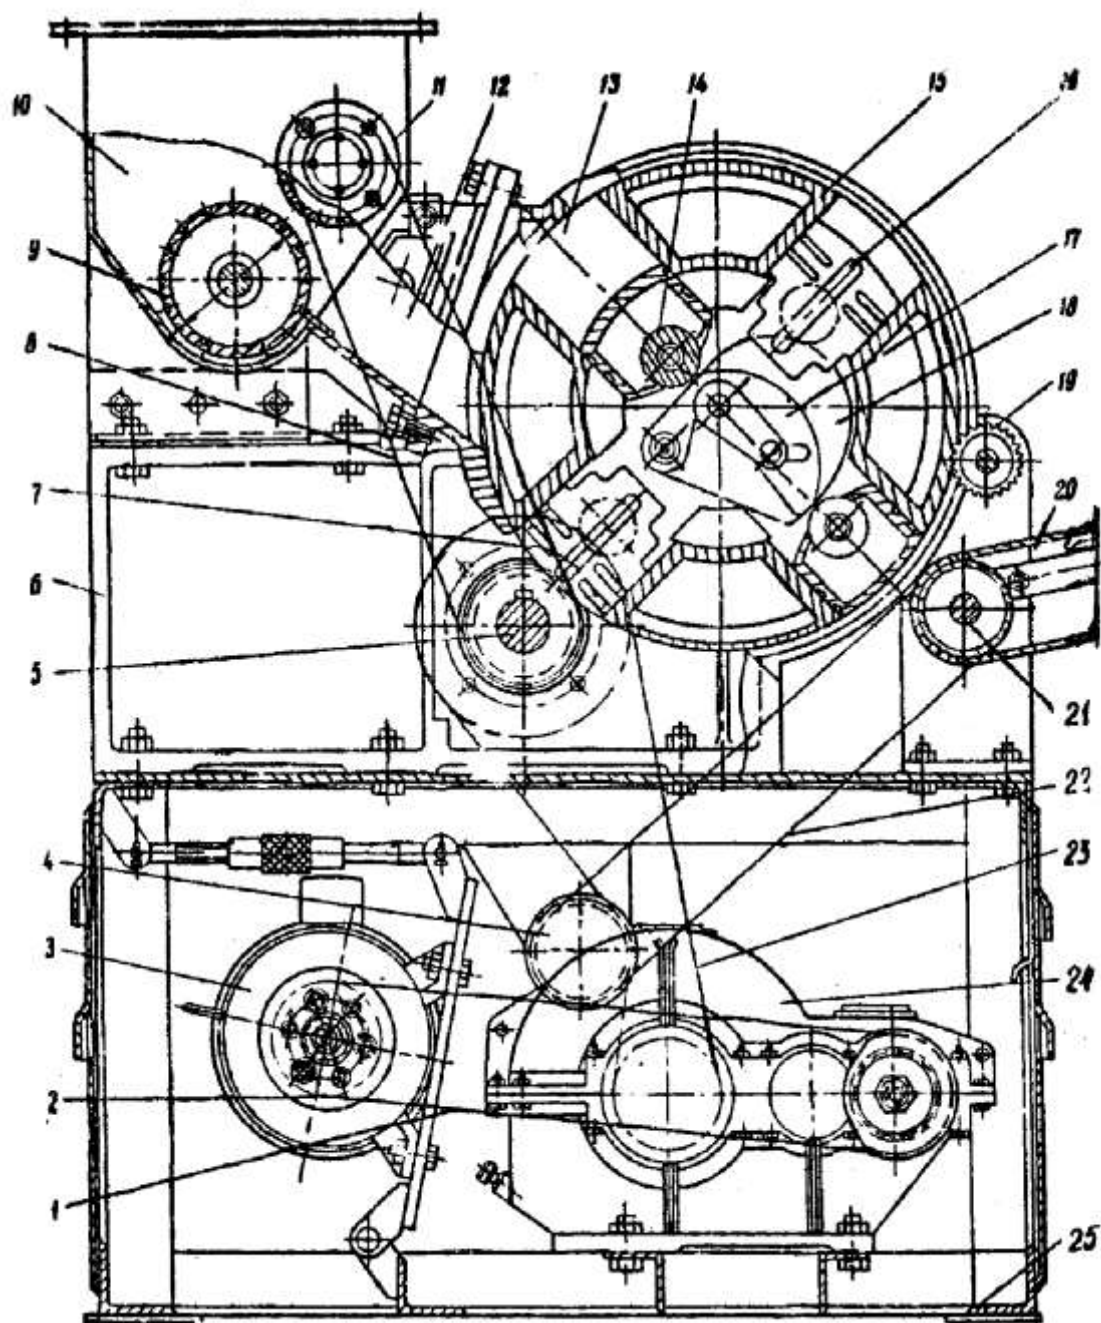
Роторний чотирьохдозаторний тісторозділювач РТ-2М:
